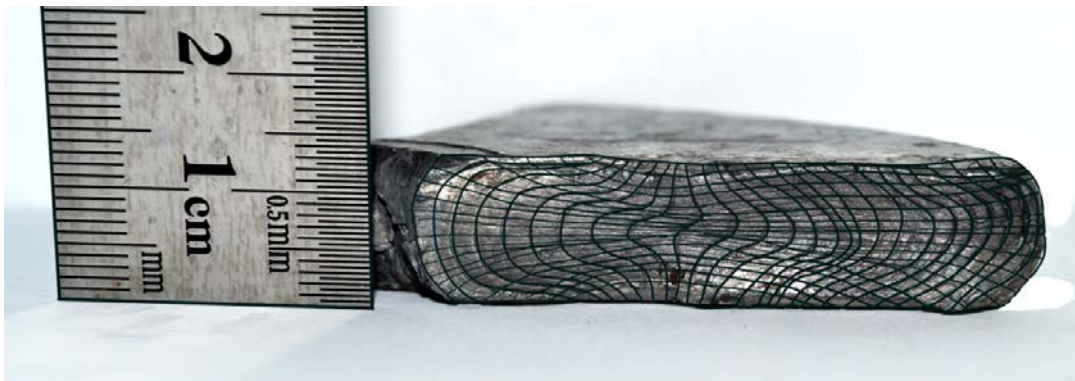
Свободная осадка между двумя плоскими шероховатыми плитами
